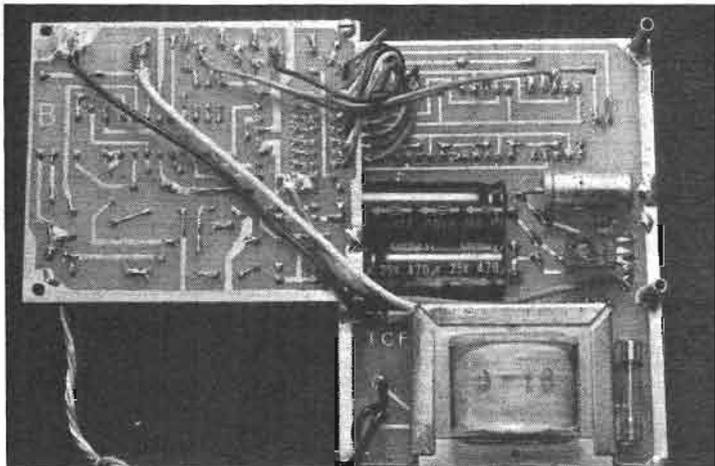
Photo E. – Disposition des deux platines pendant la pose des fils souples d'interconnexion. Noter les points de soudure des trois fils d'alimentation sur B.
